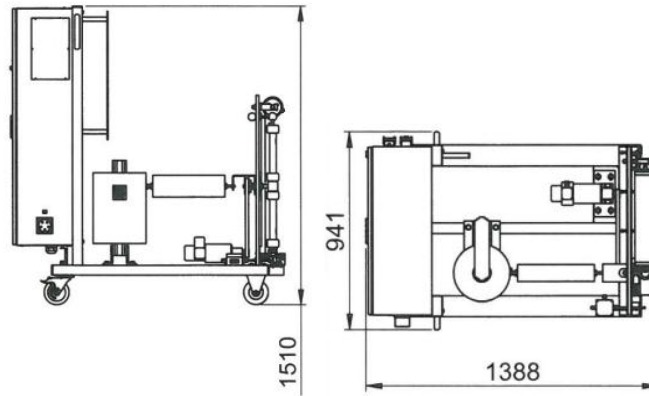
Dimensiones físicas de la unidad de carga GES 30/100E
